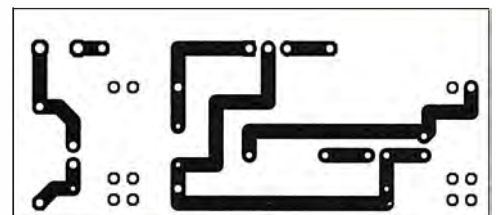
Layout der Unterseite der Aufsteckplatine für die Stromversorgung
